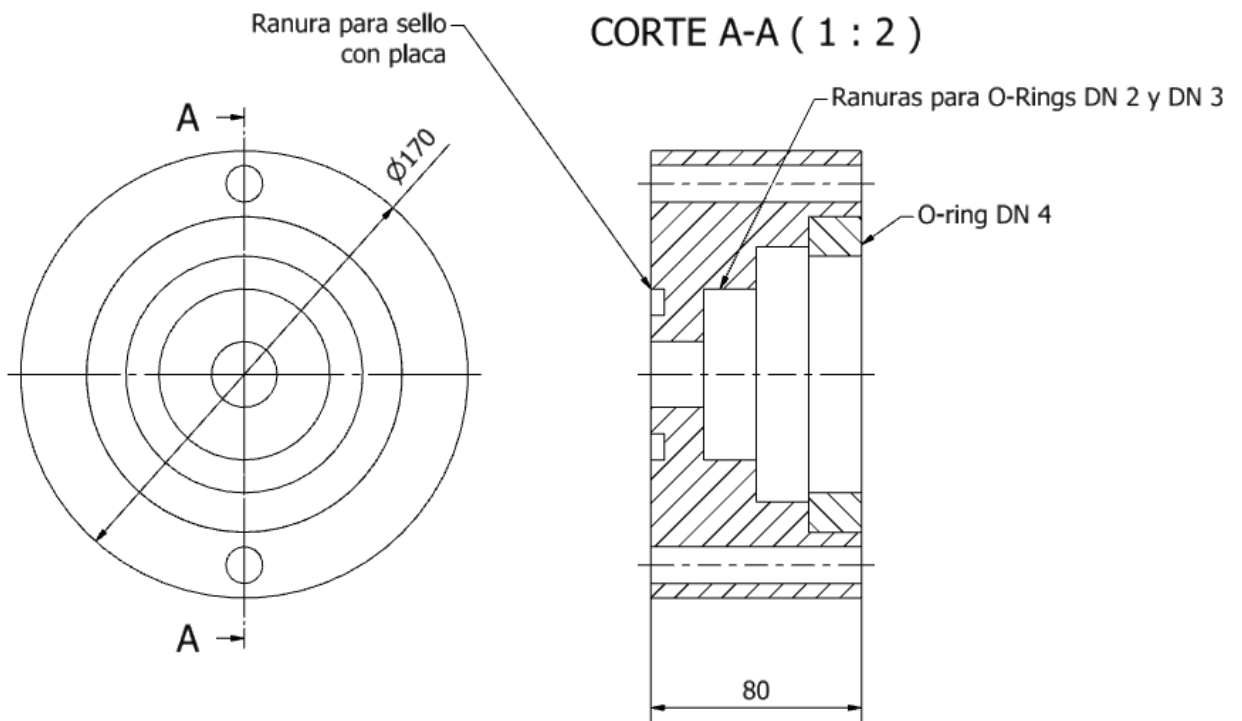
Adaptador y O-ring para válvulas DN 2 a DN 4
